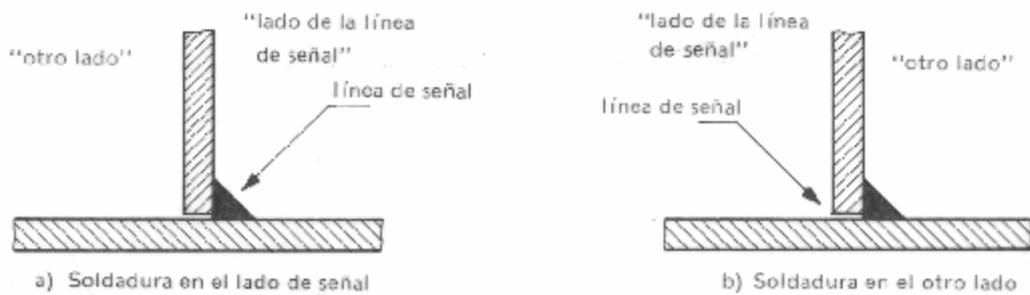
Unión T con una soldadura en ángulo.
